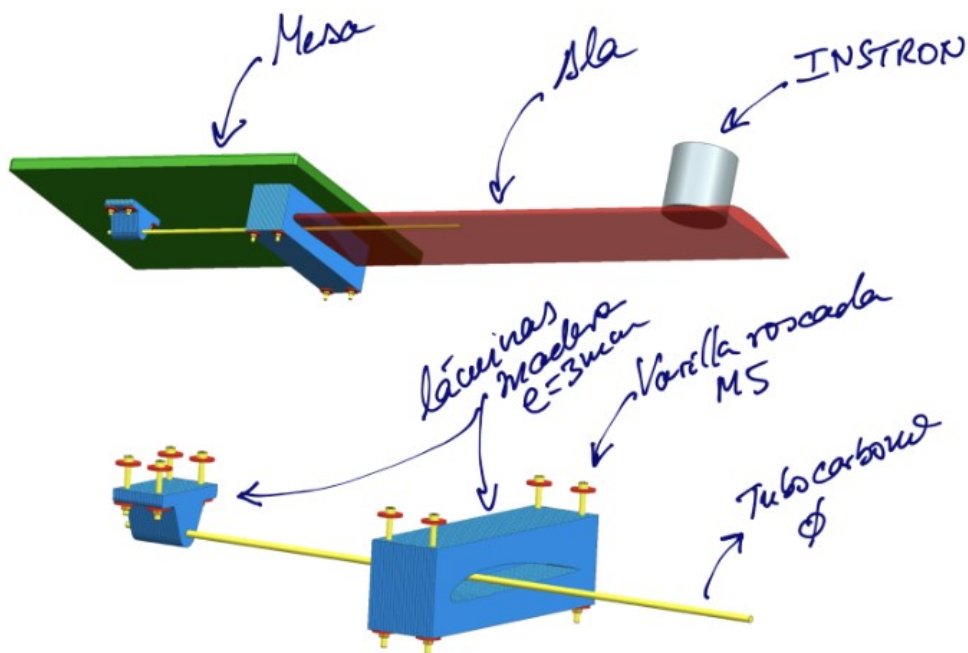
Detalle constructivo del utillaje de amarre (1/2)
